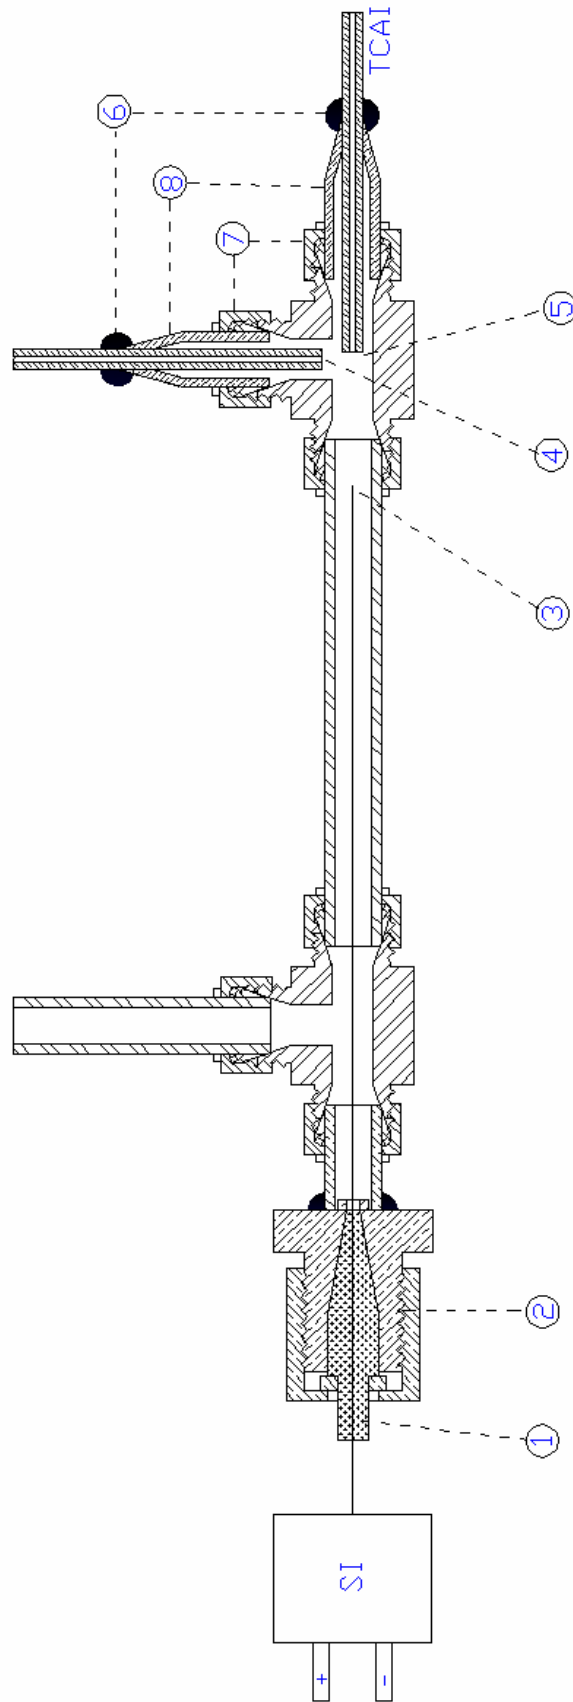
Detalhe da instrumentação na entrada do tubo capilar
